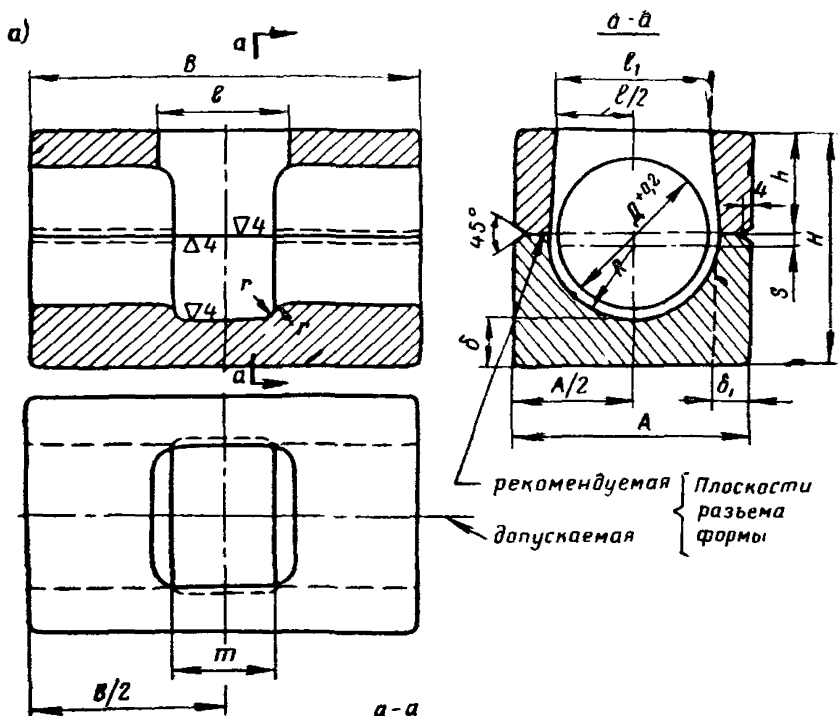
Конструкция призматических инвентарных медных форм для ванной сварки стыковых соединений однорядных стержней
